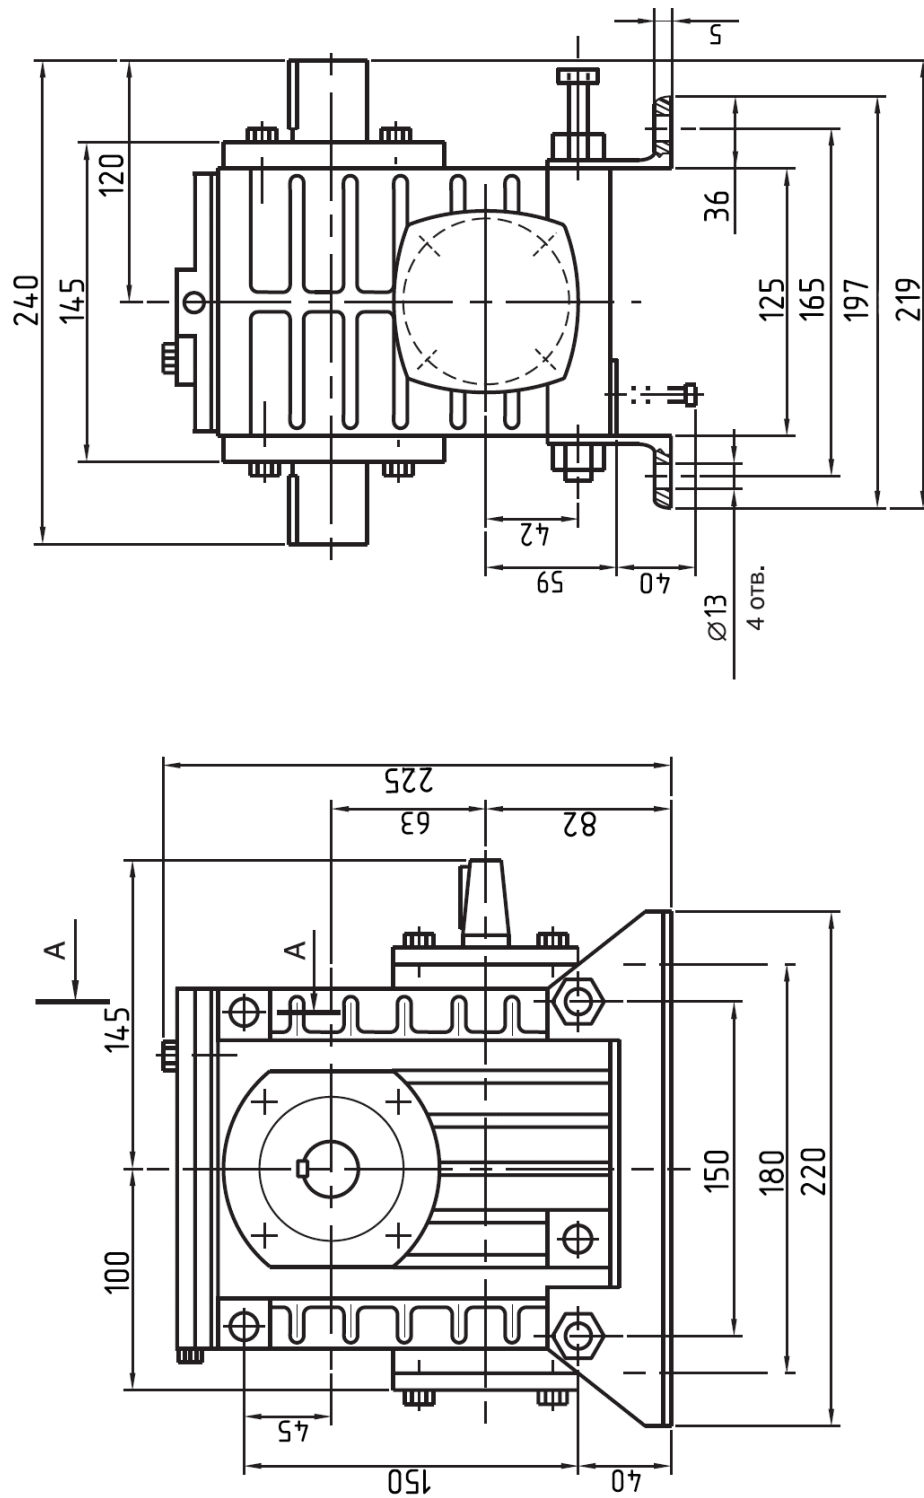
Габаритные и присоединительные размеры мотор редуктора 2Ч-63
